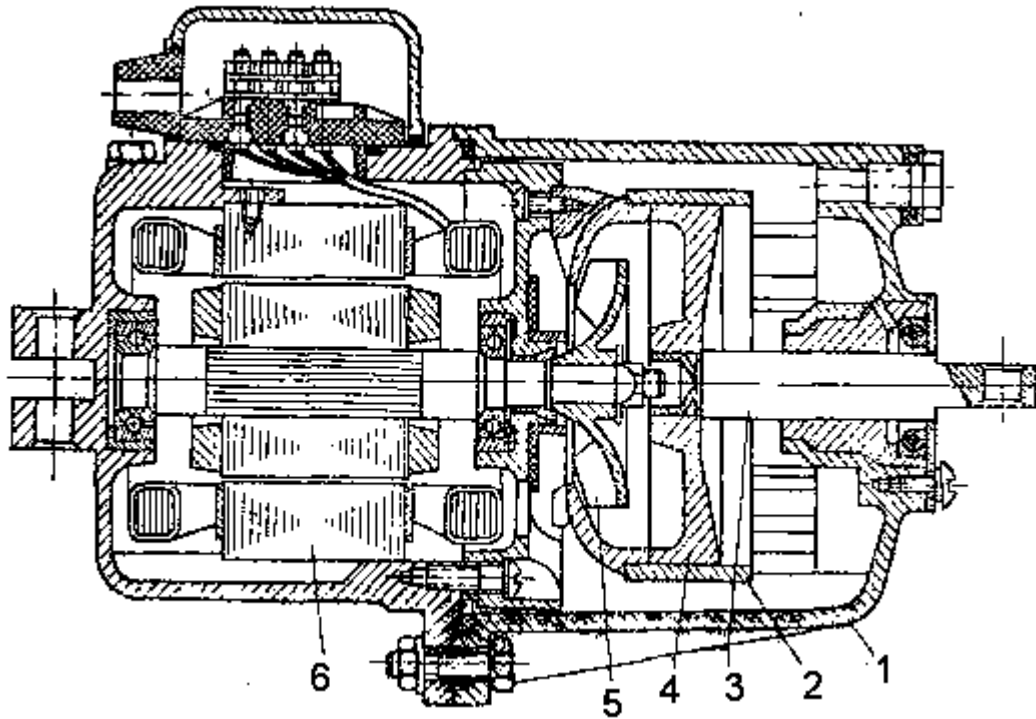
Електрогідравлічний штовхач: 1 – корпус; 2 – циліндр; 3 – шток; 4 – поршень; 5 – крильчатка насоса; 6 – електродвигун
